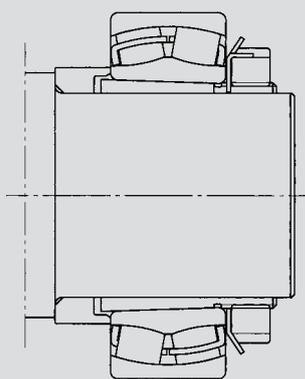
Цилиндрический вал, стопорная шайба (закрепительная втулка с дистанционным кольцом)
